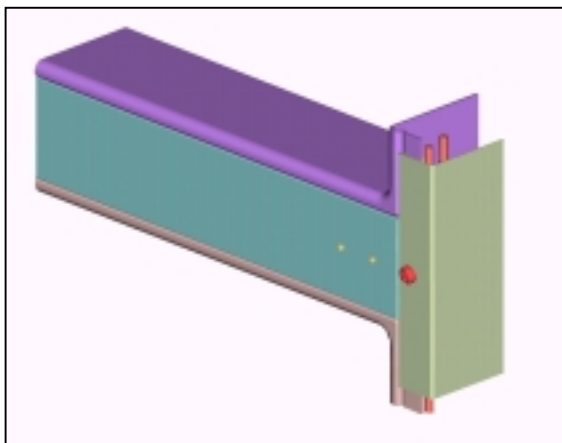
Figura A: Vista frontal da montagem do conjunto travessa intermediária.
